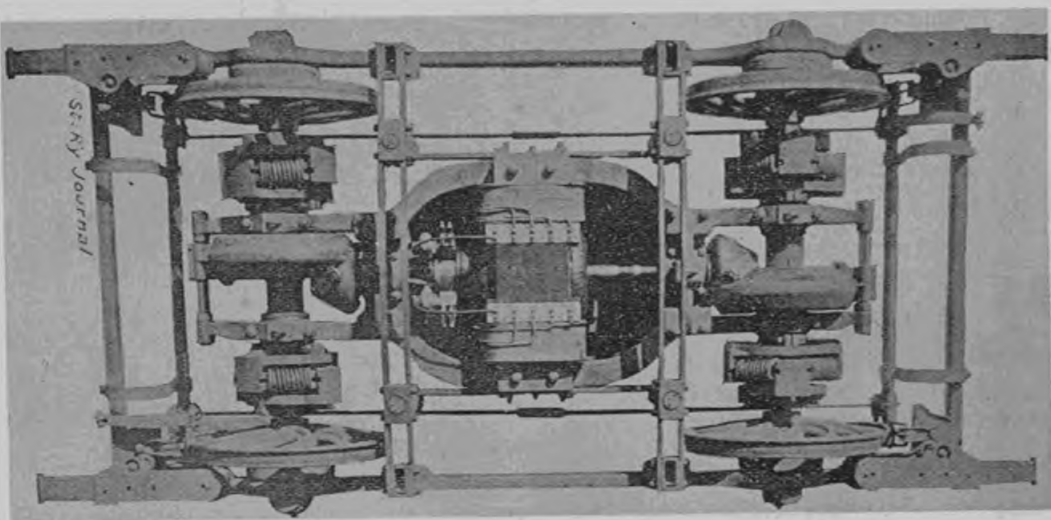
PLAN DU TRUCK MOTEUR TYPE « DETROIT »
